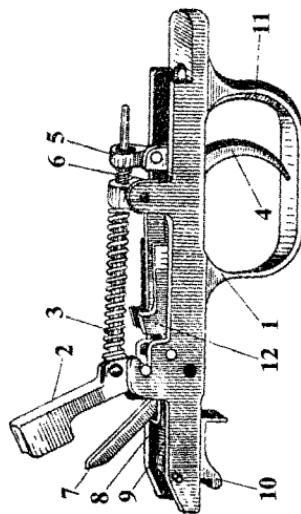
Ударно-спусковой механизм СКС: 1 — спусковая скоба; 2 — курок; 3 — боевая пружина; 4 — спусковой крючок; 5 — спусковой рычаг; 6 — спусковая пружина; 7 — автостоп; 8 — шептала; 9 — пружина шептала; 10 — защелка магазина; 11 — защелка магазина; 12 — разобщитель-таль.
